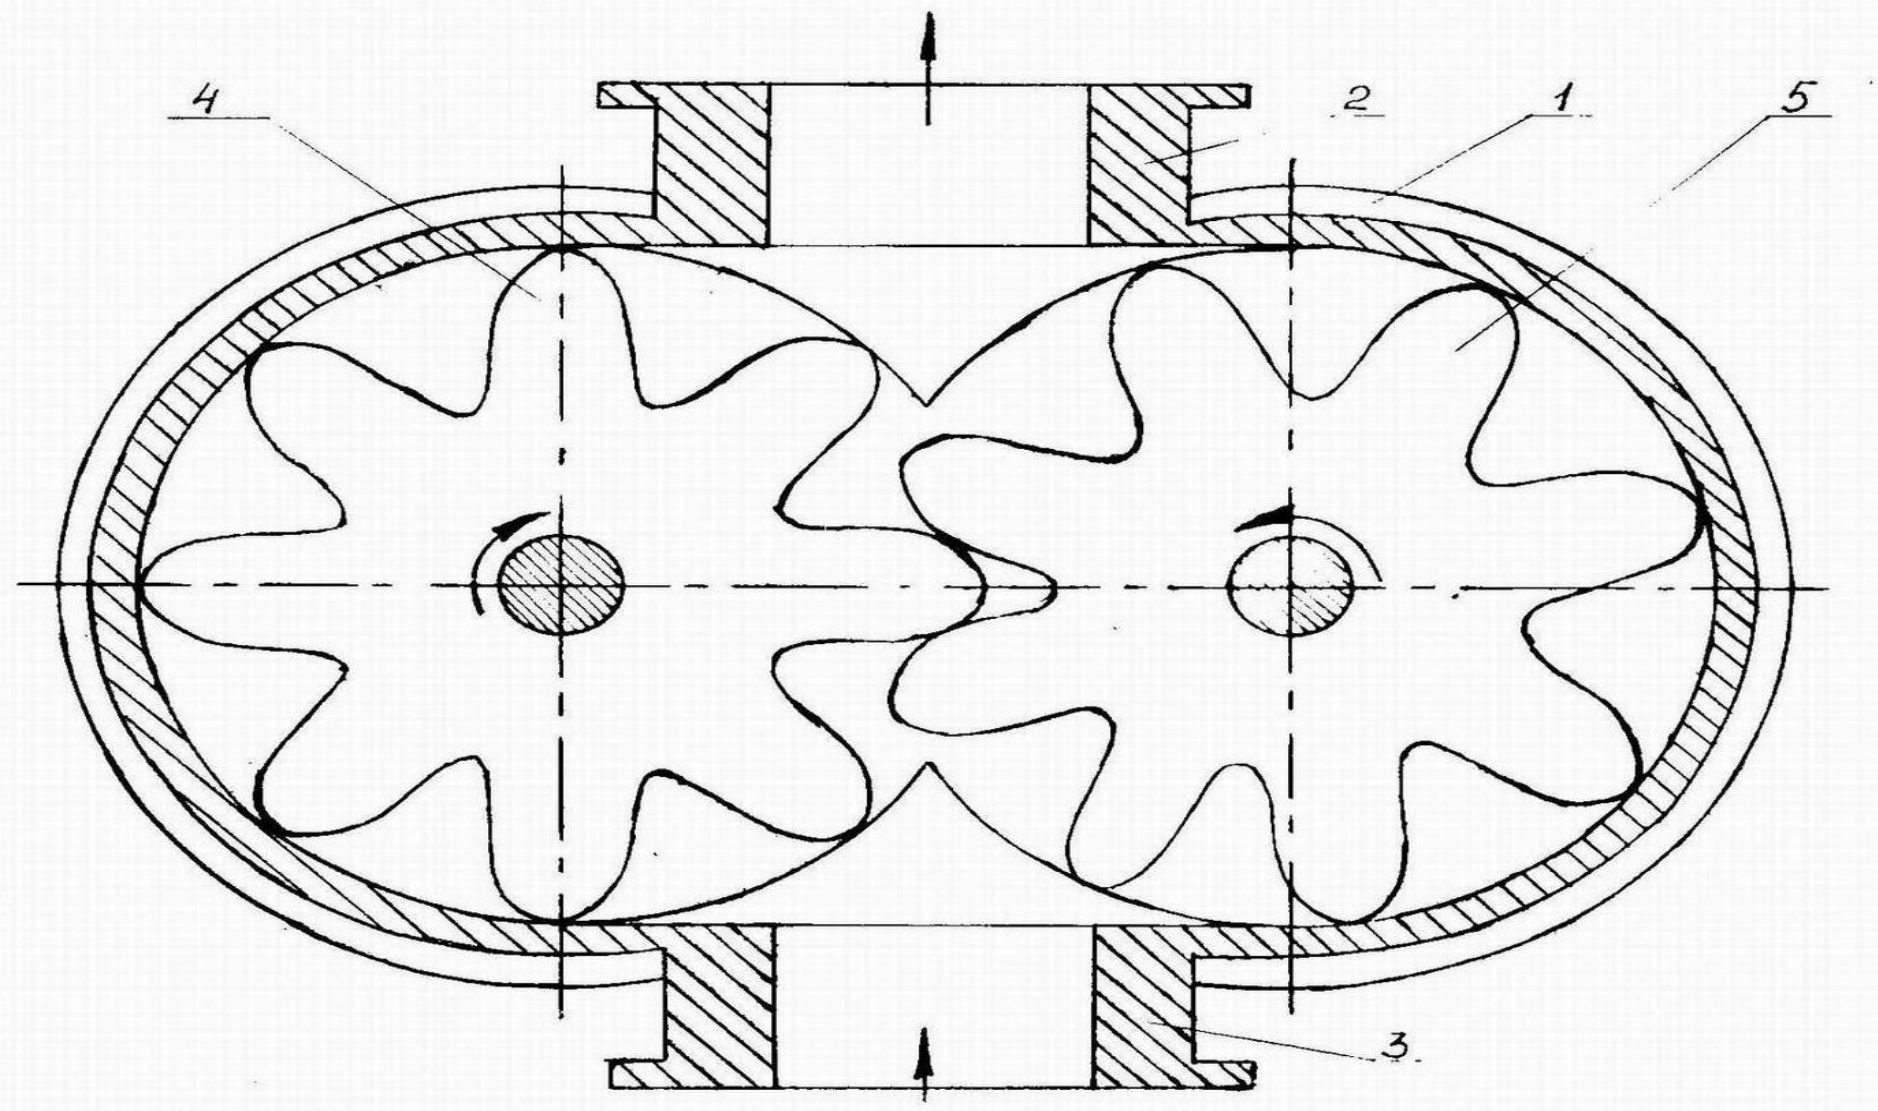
Схема шестиренчатого насоса: 1 – корпус; 2 – нагнетательный патрубок; 3 – всасывающий патрубок; 4,5 – шестерни;
